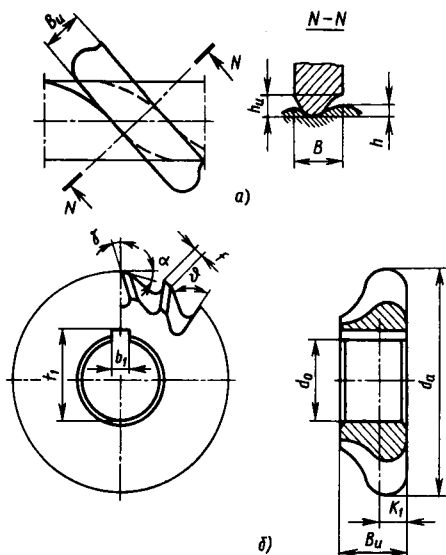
Положение инструмента относительно заготовки и общий вид дисковой фрезы
